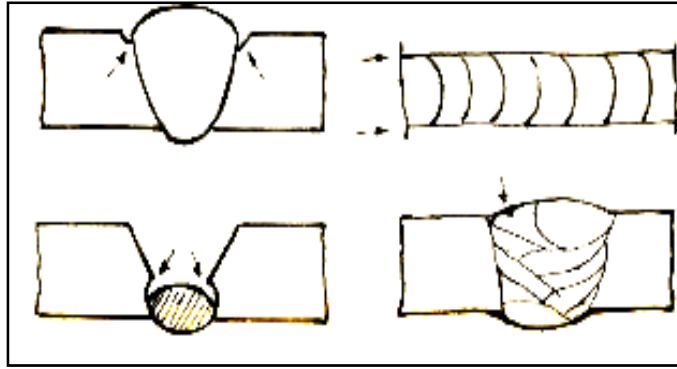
Varias formas de mordeduras en soldadura
